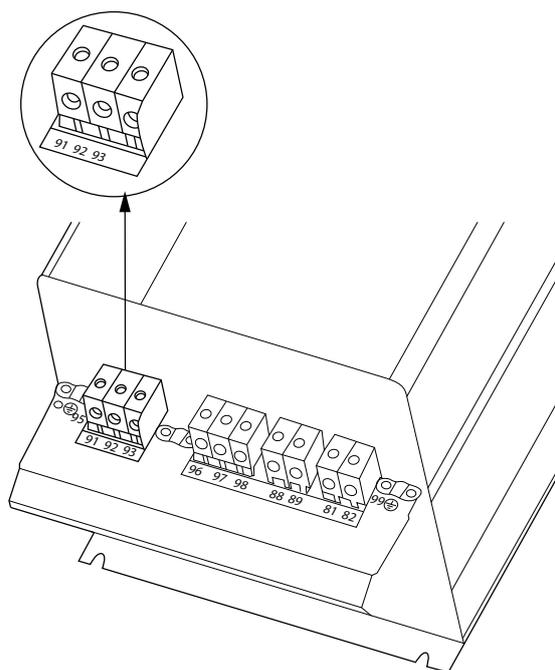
Raccordement au secteur des protections de taille C3 (IP20)
